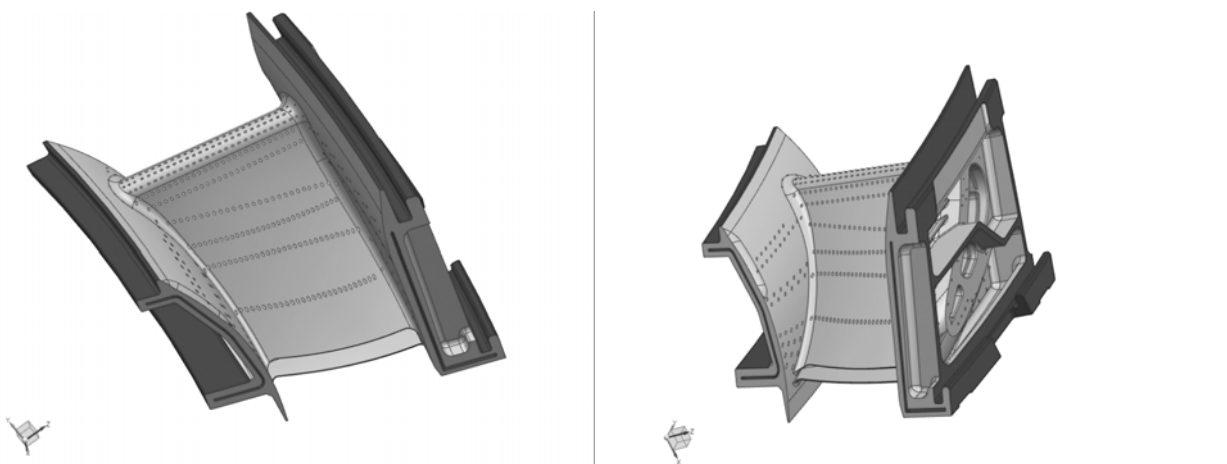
Расположение базовых поверхностей и перфорационных отверстий сопловой лопатки 1-й ступени ГТД.
